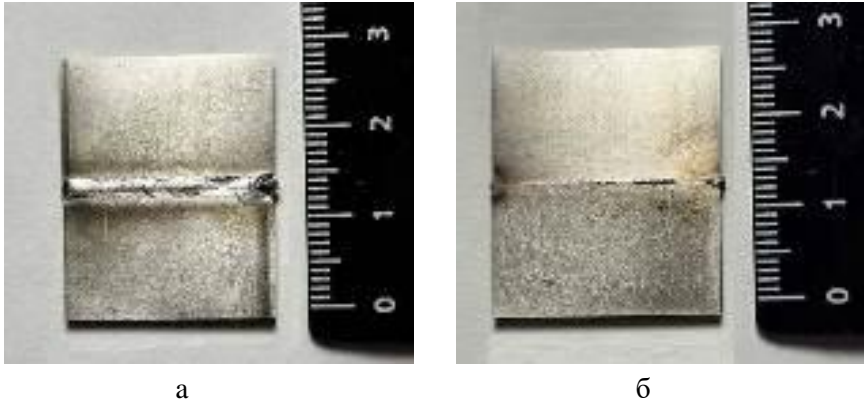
Внешний вид сварного соединения из сплава ВТИ-4, полученного электронно-лучевой сваркой: а) валик сварного шва; б) корень сварного шва.
